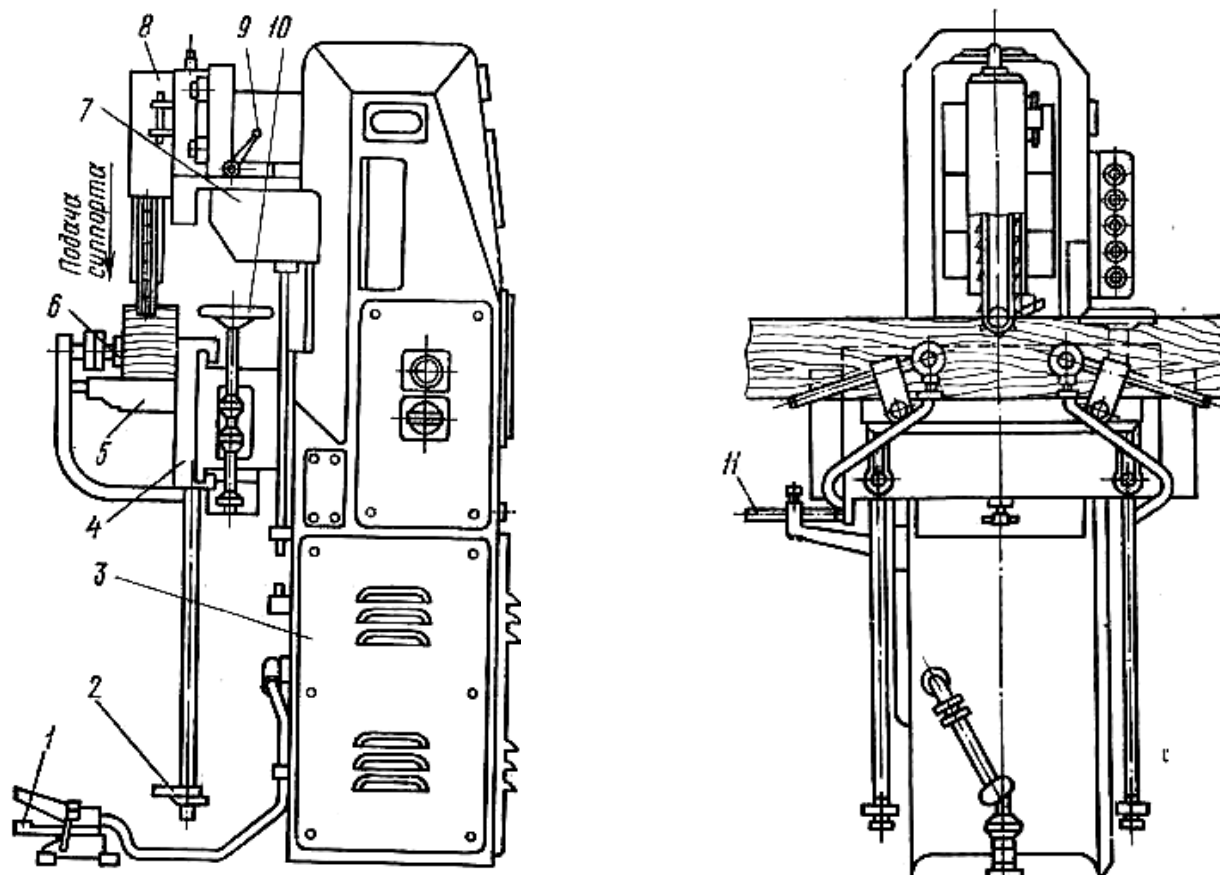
Цепнодолбежный универсальный станок ДЦА-4: 1 — педаль, 2 — упор, 3 — станина, 4 — вертикальная плита, 5 — горизонтальная плита, 6 — гидropriжим, 7 — суппорт, 8 — режущая головка, 9 — рукоятка, 10 — маховичок продольной подачи, 11 — ограничитель хода стола
